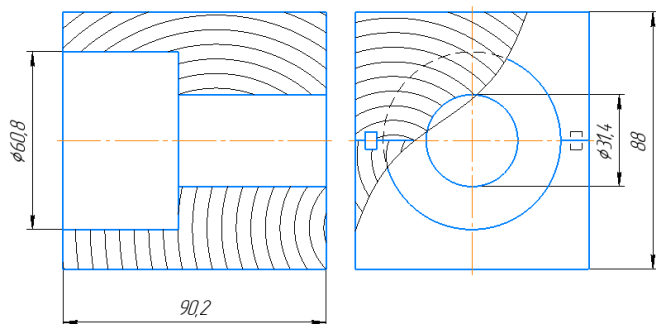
Стержневой ящик для изготовления детали «штуцер» (эскиз)
